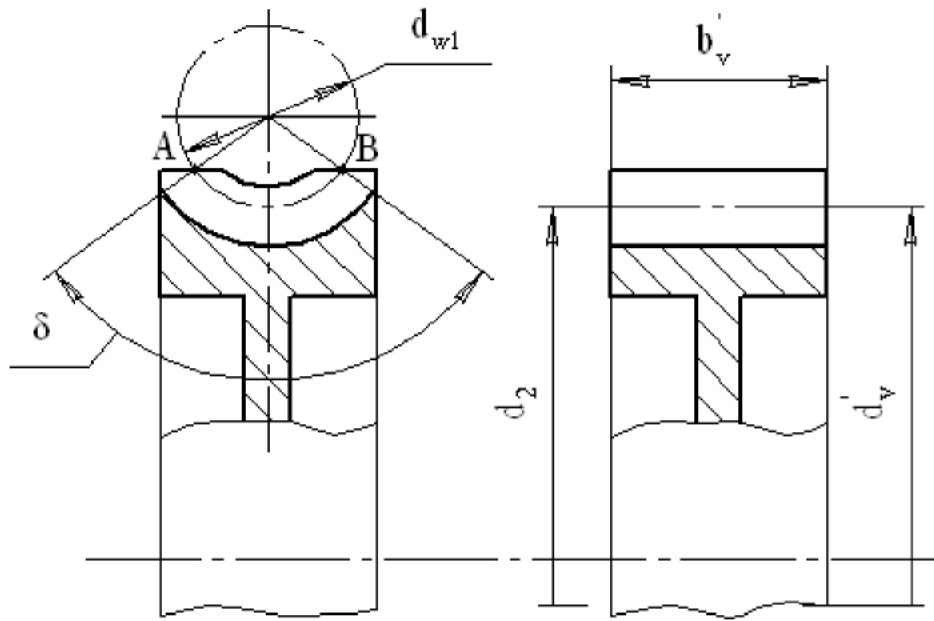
Схема формирования размеров цилиндрического колеса, эквивалентного червячному
